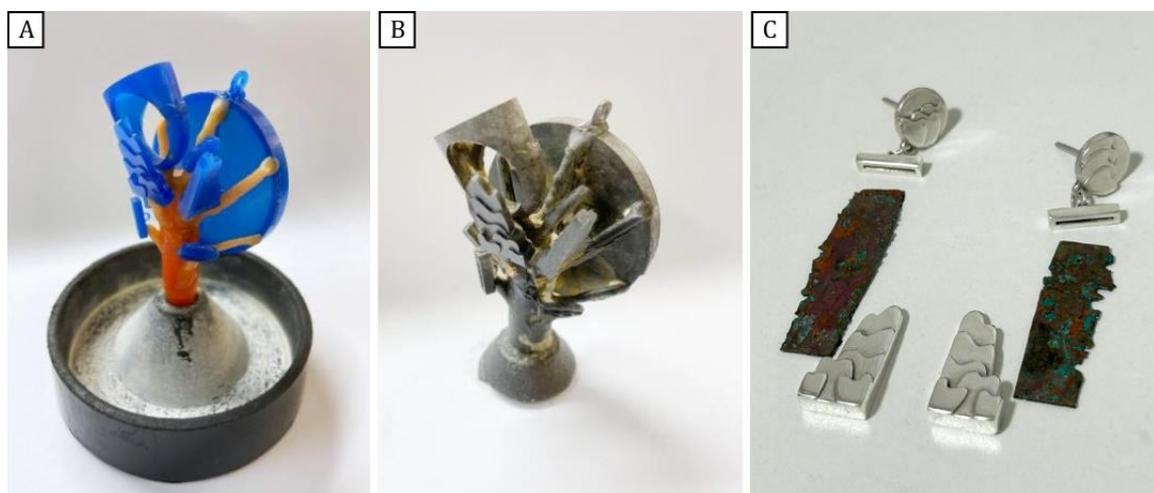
Processo de fabricação: (A) árvore de usinagem em cera, (B) fundição finalizada e (C) peças prontas para a montagem final. Fonte: Autores (2025).
